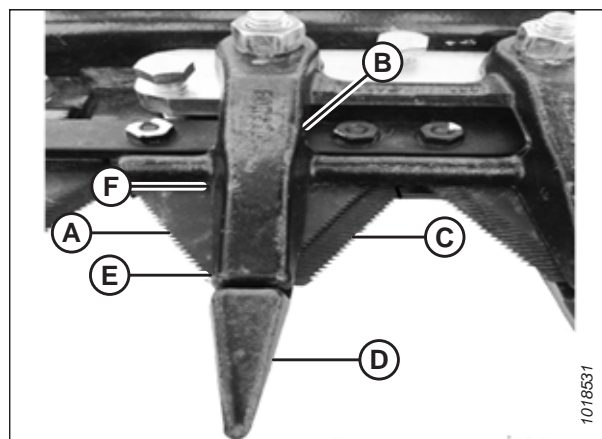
Прижим центрального противорежущего пальца двойного ножа
